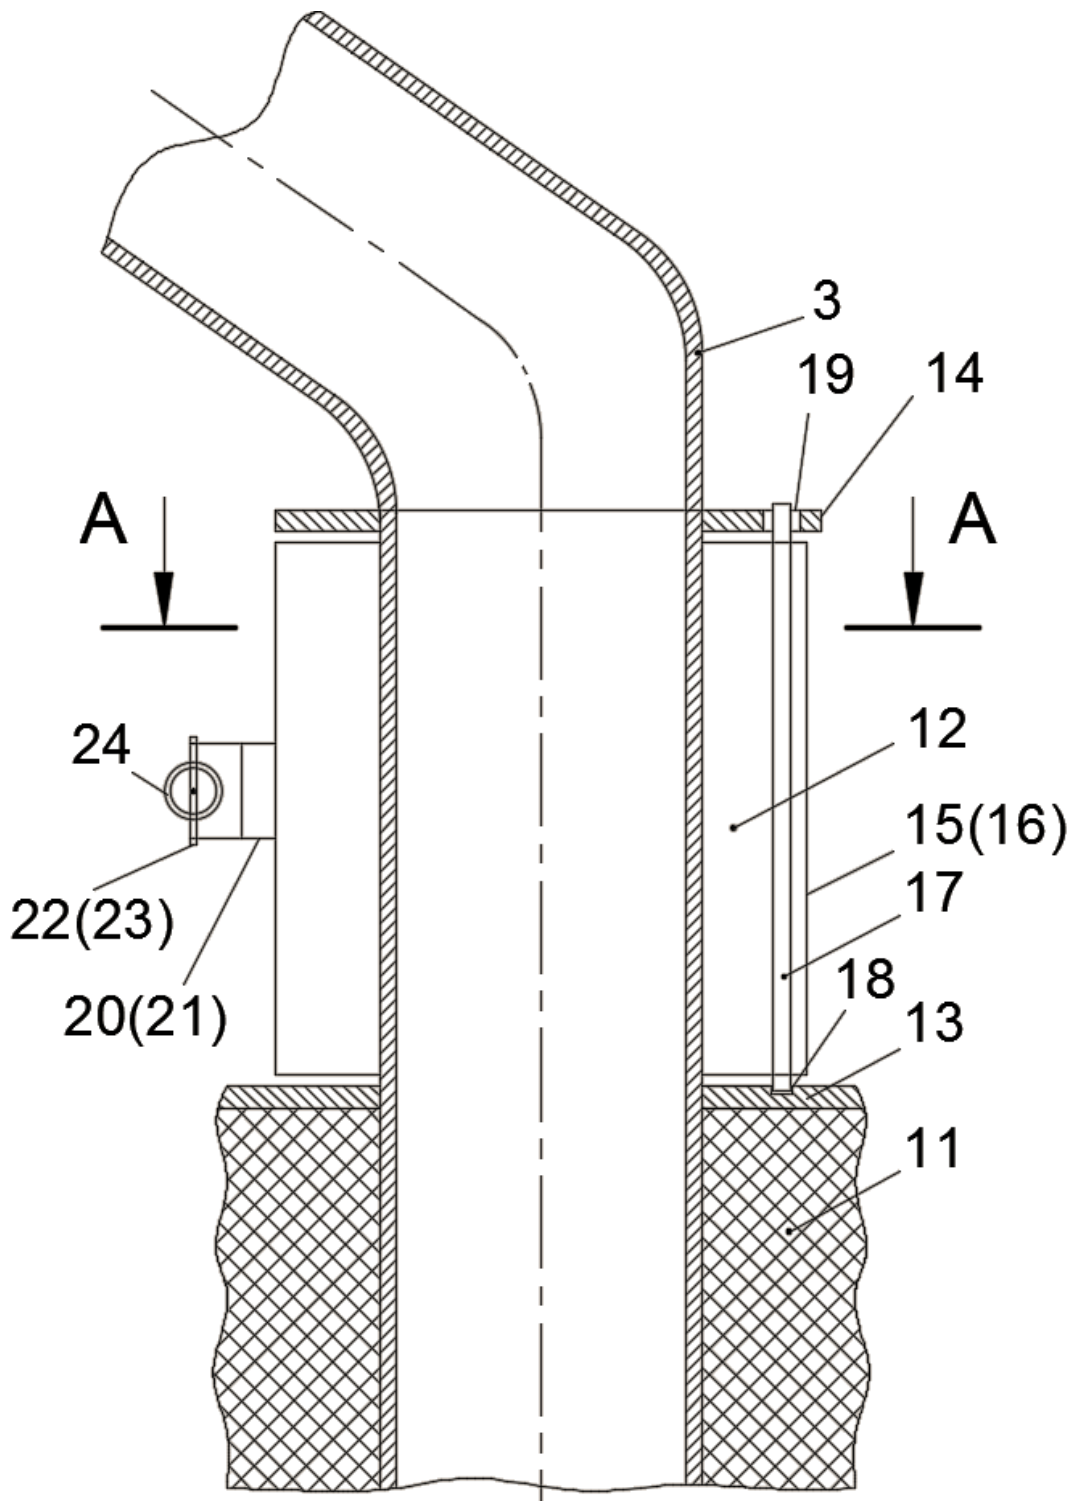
Схема підйомної ділянки дефлегматора з додатковим роз'ємним кожухом: 3 – підйомна ділянка дефлегматора; 11 – теплоізоляційний кожух генераторного вузла; 13 і 14 – шайби кріплення додаткового кожуха; 15 і 16 – стулки додатково кожуха; 17 – вісь кріплення додаткового кожуха; 18 – паз для вісі; 19 – отвір для вісі; 20 і 21 – напівовальні пластини; 22 і 23 – вісі кріплення; 24 – сиффон
